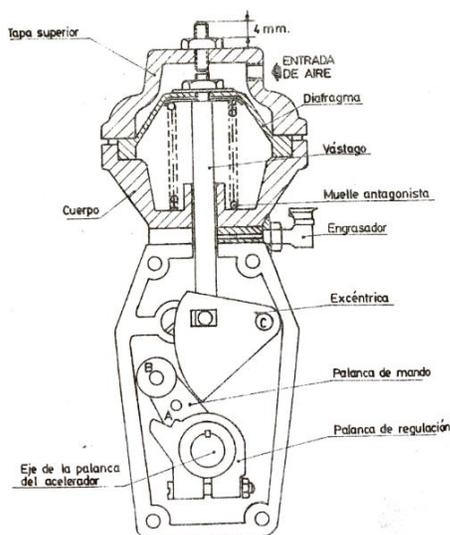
Partes principales de la bomba PE con variador de avance y corrector de humos instalado en el cárter regulador
